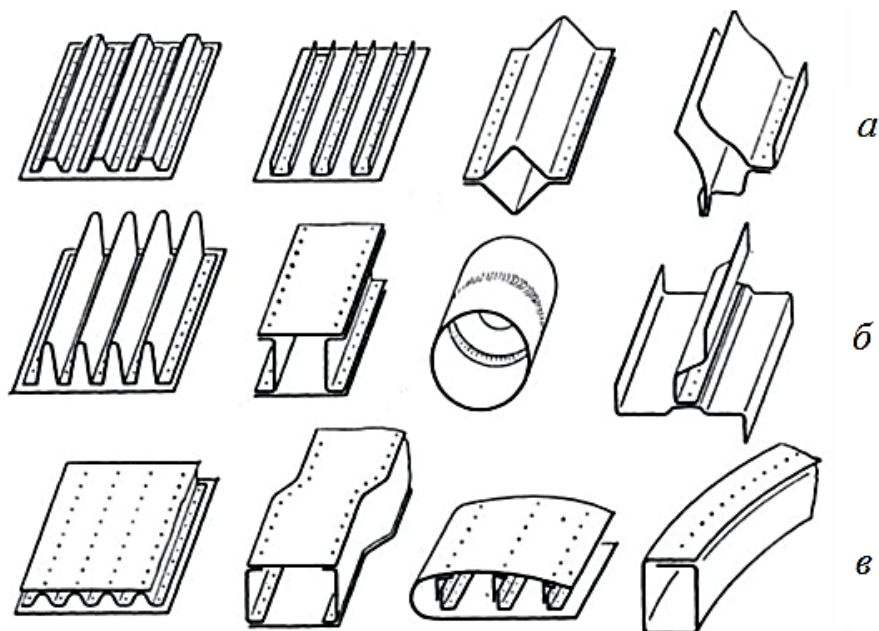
Варианты конструкции узлов, выполняемых точечной и шовной сваркой
